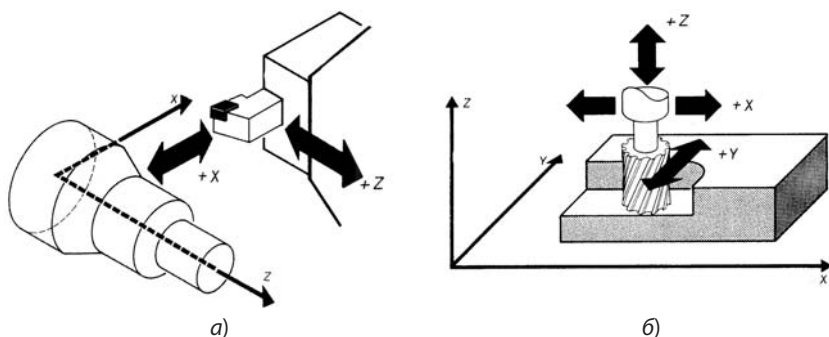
Системы координат с обозначением положительных направлений прямых перемещений рабочих органов с инструментом:
